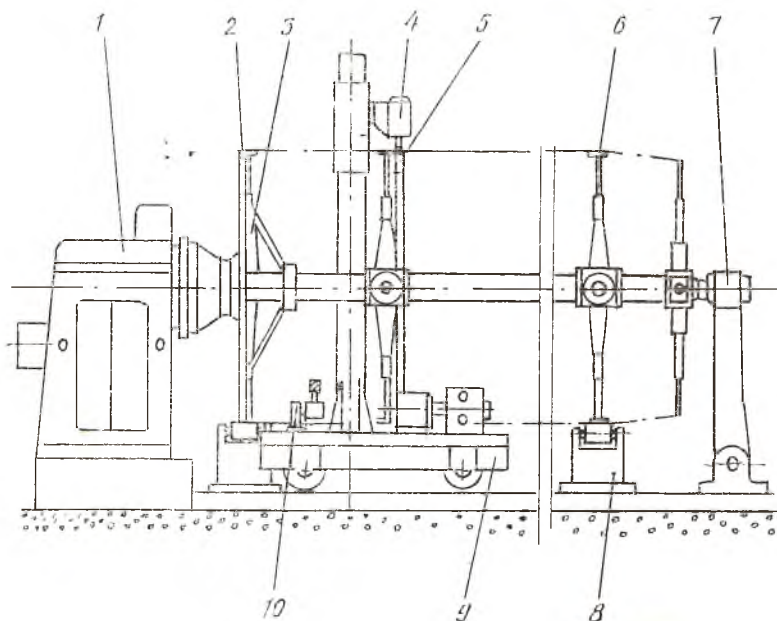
Схема сварочного стэнда: 1 — передняя бабка; 2 — планшайба; 3 — разжимное центрирующее устройство; 4 — головка для АДЭС; 5 — подкладное кольцо; 6 — разжимное кольцо; 7 — задняя бабка; 8 — люнет; 9 — подвижный портал; 10 — фрезерная головка
